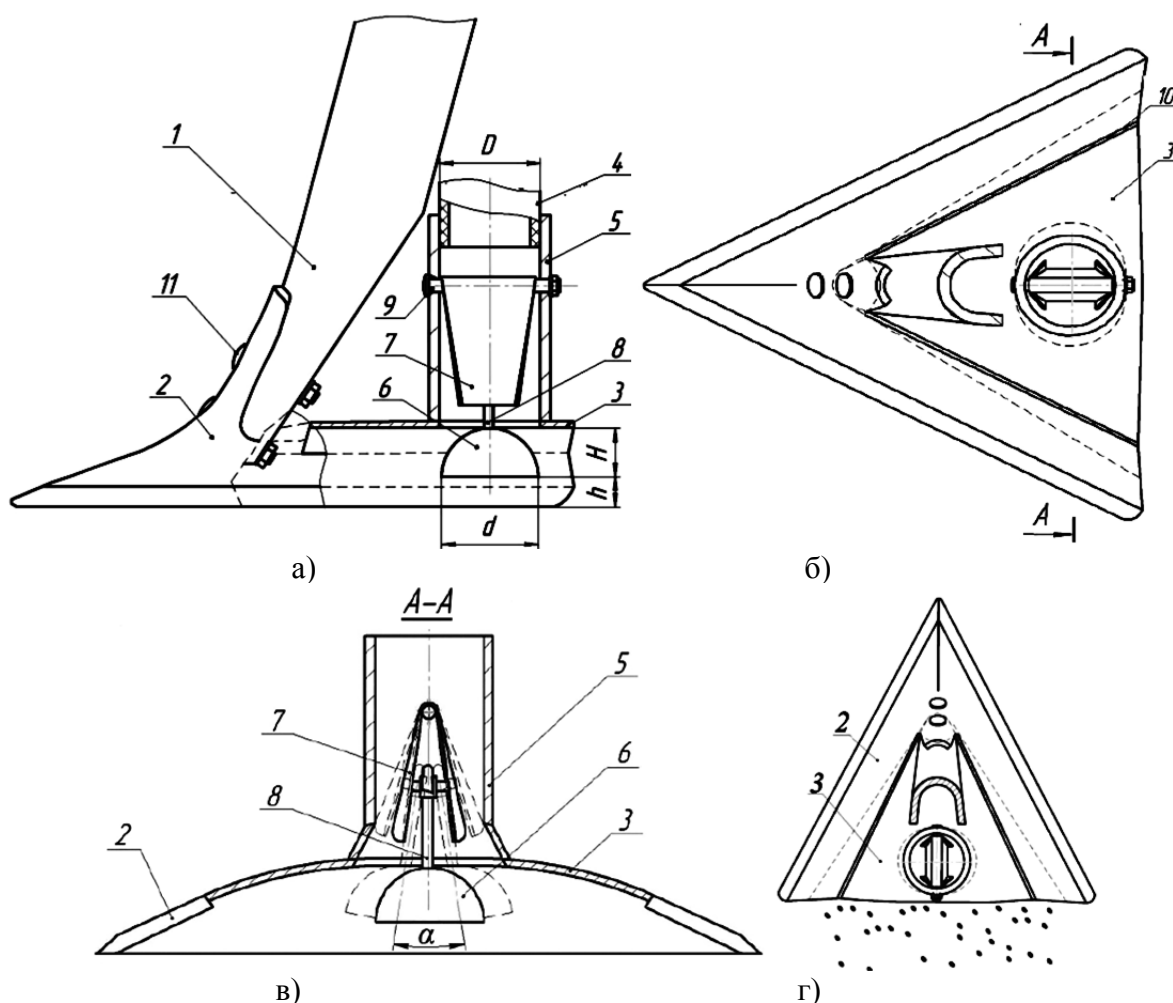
Сошник для подпочвенно-разбросного посева: а – вид сбоку; б – вид сверху; в – распределитель; г – схема расположения семян и удобрений
